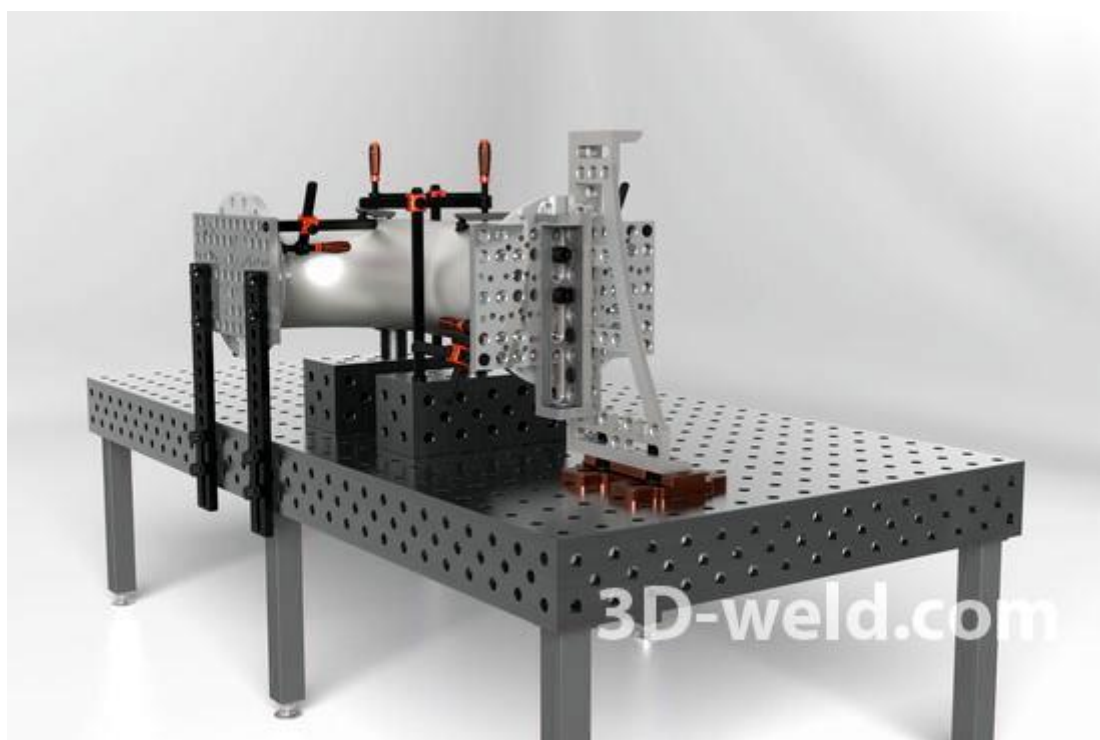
Сварочный стол 3D-Weld SOLID D16 1500x3000мм [20]
